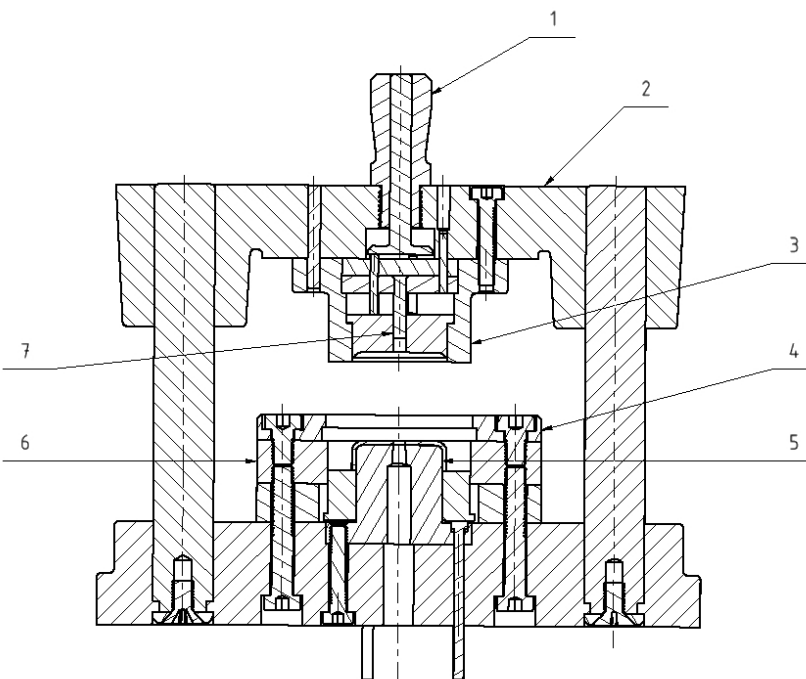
Schneid- und Ziehwerkzeug für Kappe mit Bohrung
